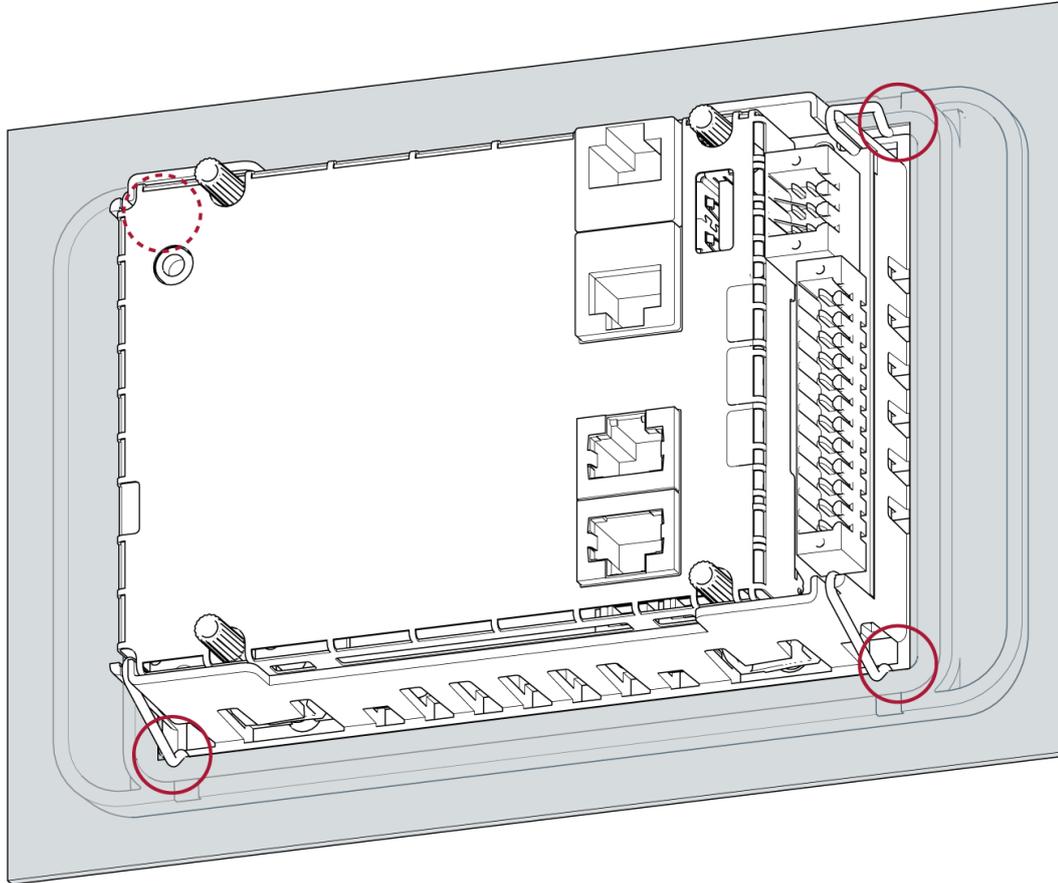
Gerät im Montageausschnitt eingerastet, Beispiel mit 4 Befestigungsklammern
